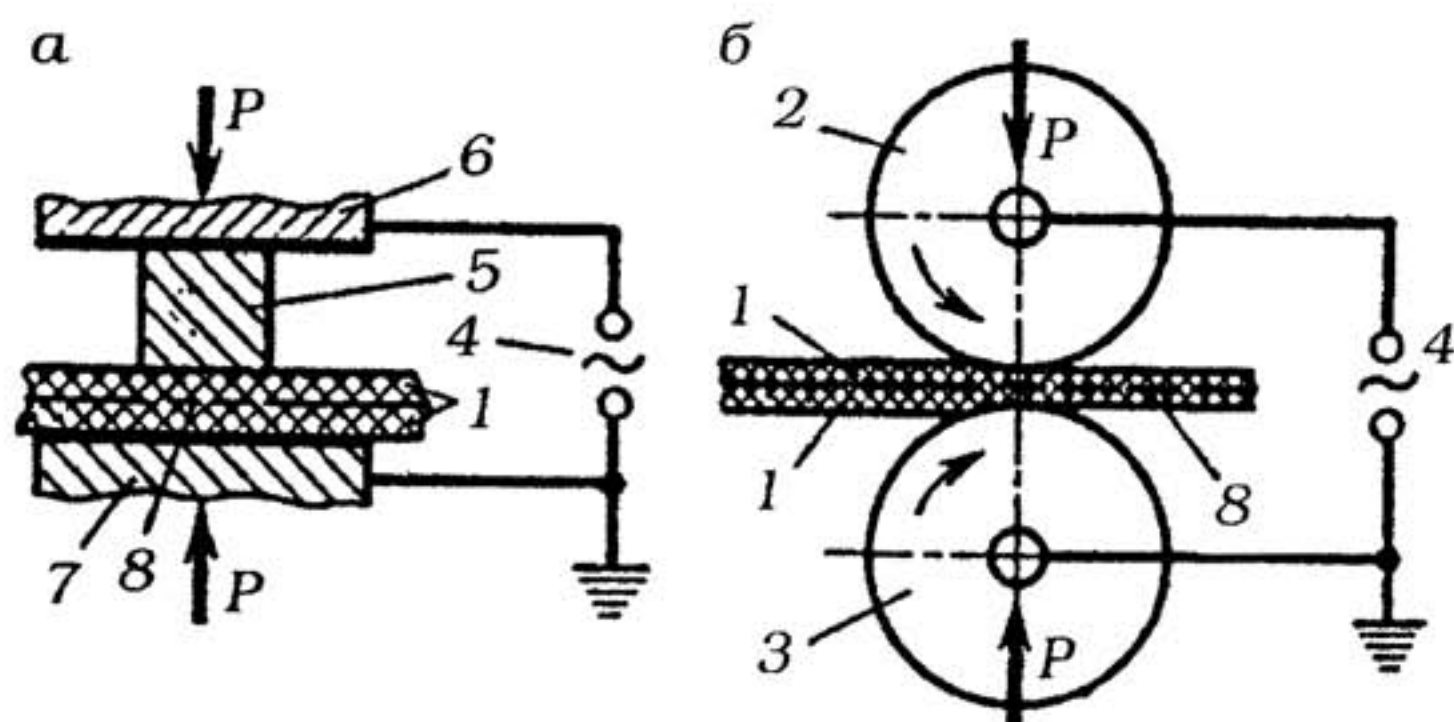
Прессовая (а) и роликовая (б) высокочастотная сварка полимерных пленок: 1 — свариваемые материалы; 2 — высокопотенциальный ролик; 3 — заземленный ролик; 4 — генератор высокой частоты; 5 — рабочий инструмент; 6 и 7 — обкладки рабочего конденсатора (6 — высокопотенциальная, 7 — заземленная); 8 — сварной шов
